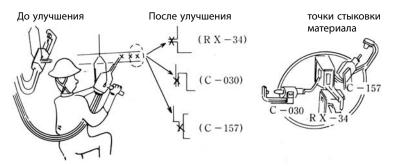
Выбор инструмента при точечной сварке кузовов
